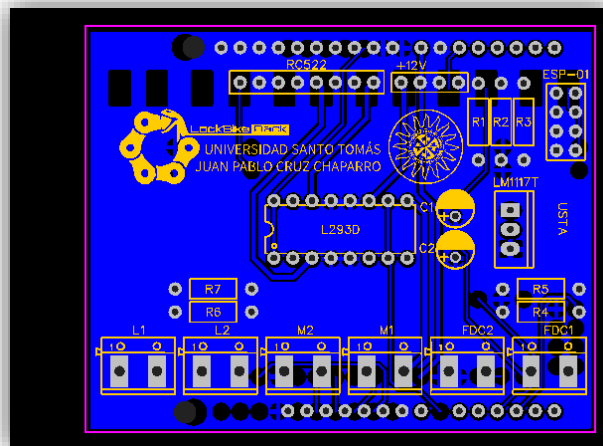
Diseño conexiones capa inferior PCB, impresión – LockBikeRack
